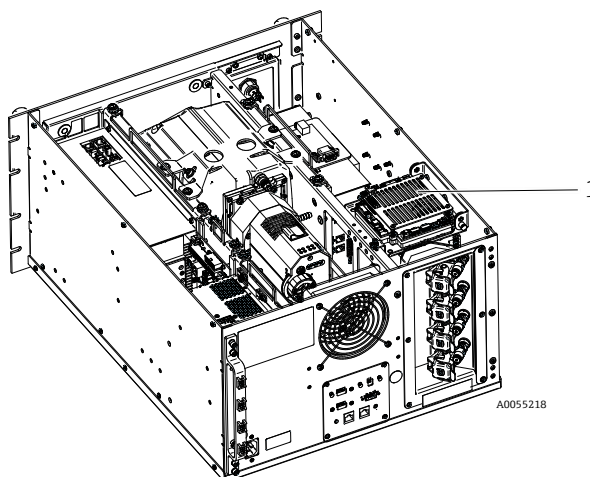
Vue d'ensemble arrière avec plaque de contrôleur en position normale (1)
